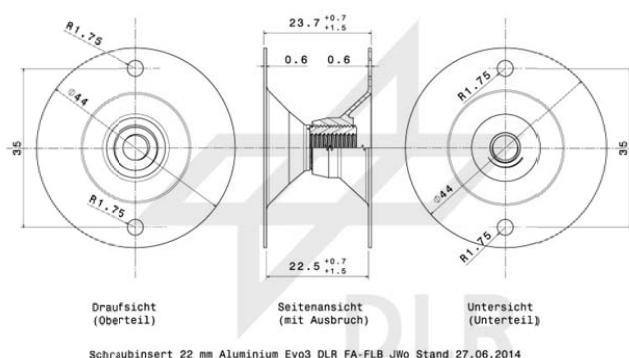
Dimensionsmaße des Insertprototyps Schraubinsert Aluminium, 22 mm (für Sandwichtyp 618 HC)
